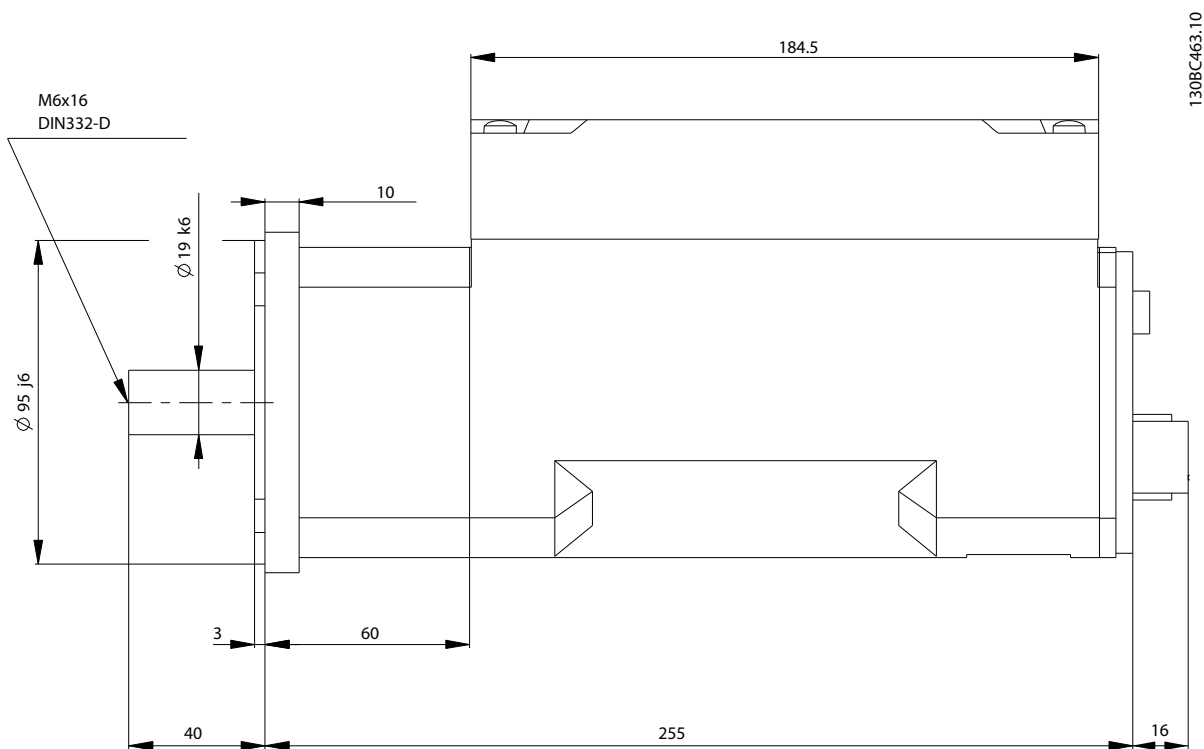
Seitenansicht: Servomotor mit ISD Flansch und Bremse
